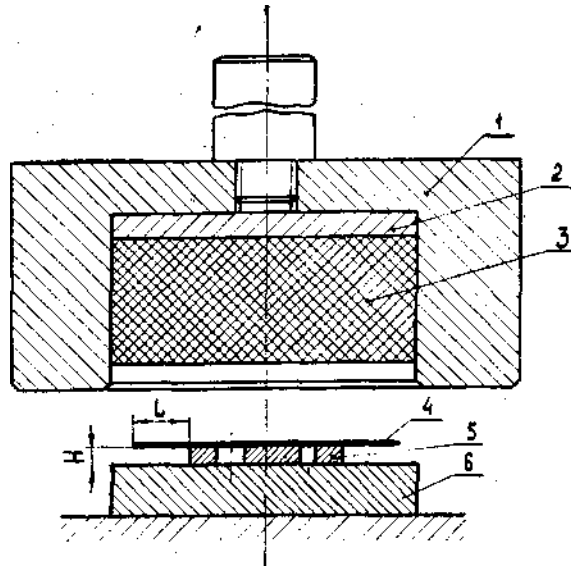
Схема виробування, пробивання. 1 - контейнер; 2 - металева шайба; 3-поліуретанова пластина; 4 - заготовка; 5 -вирізний шаблон; 6 - підштампова плита.
